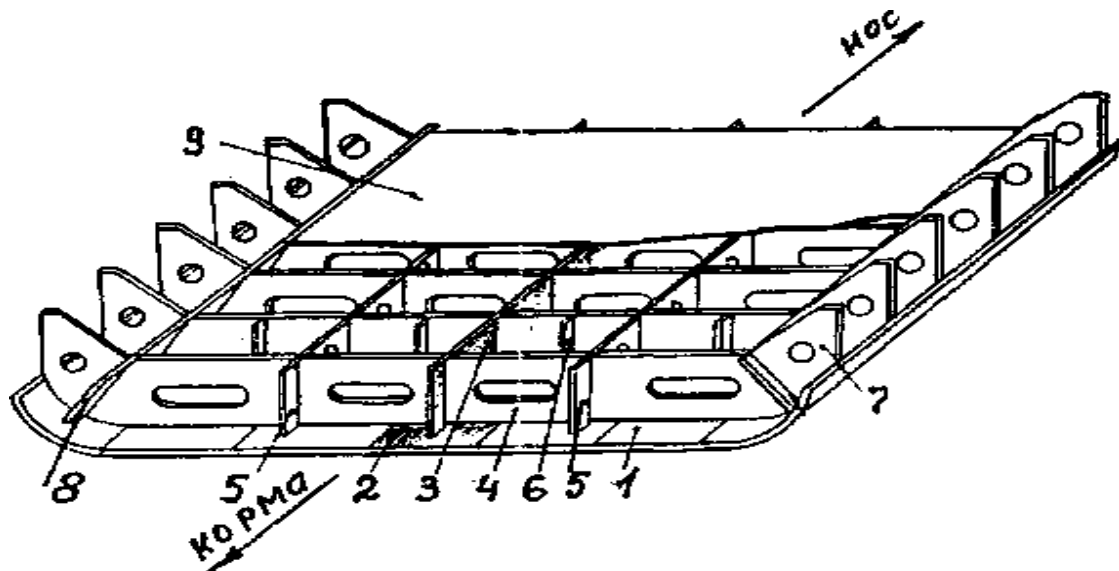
Конструкция днищевого перекрытия с двойным дном при поперечной системе набора: 1 - наружная обшивка днища; 2 – горизонтальный киль; 3 - вертикальный киль; 4 - сплошной флор; 5 - днищевой проницаемый стрингер; 6 - ребро жесткости; 7 - скуловая кница; 8 - крайний междудонный лист; 9 -настил второго дна
